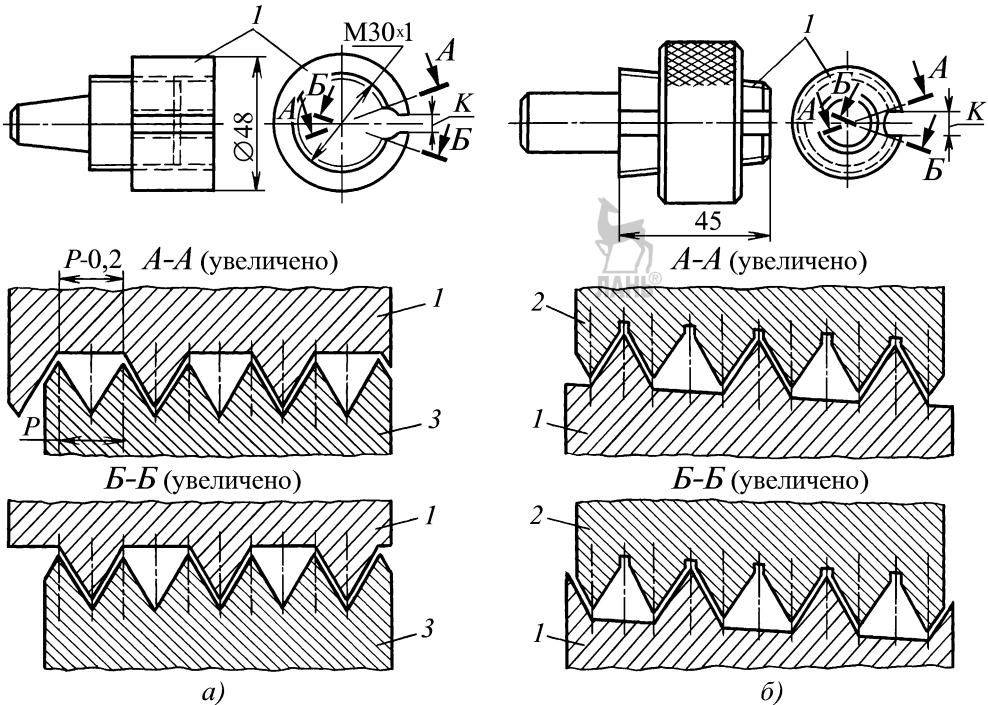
Схема доводки резьбовых цилиндрических (а) и конусных (б) калибров притиром с удаленной через шаг ниткой резьбы:
